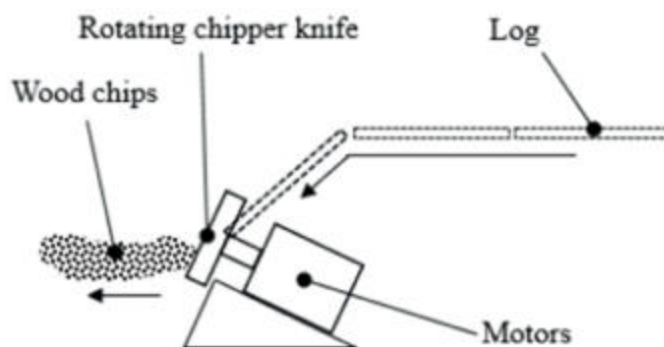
Подрібнювач деревини: wood chips – деревні тріски; rotating chipper knife – обертовий ніж-подрібнювач; motors – двигуни; log – поліно.
